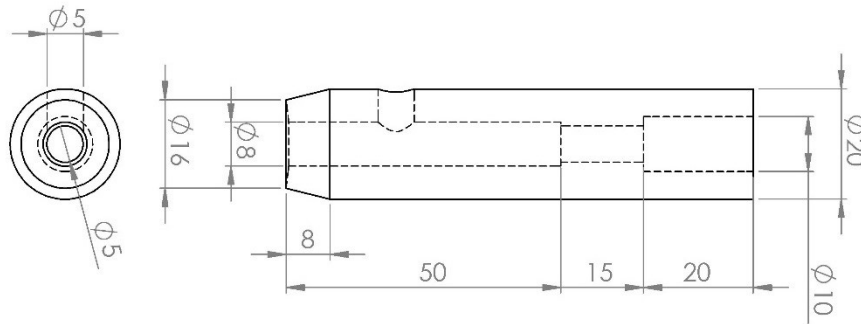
Desenho técnico do *shoulder* para a ferramenta da 3ª abordagem tecnológica.
